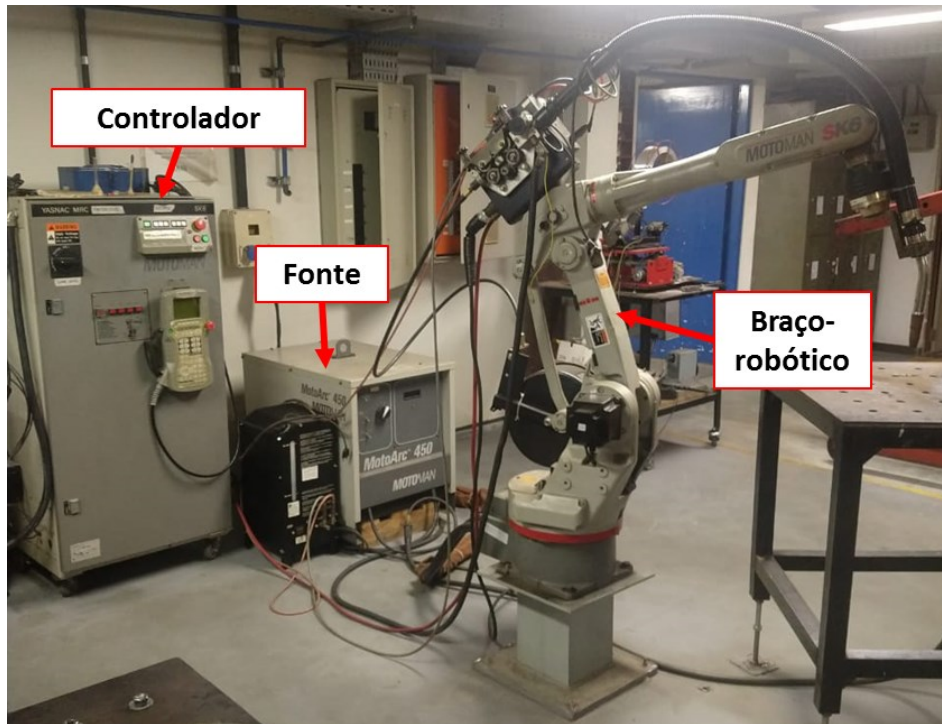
Braço robótico, controlador e fonte utilizados na soldagem GMAW (Próprio autor)
